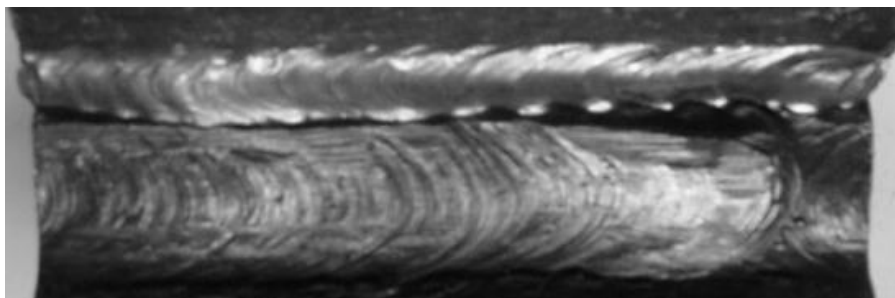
Cordão de soldadura típico dos provetes da série PDR.
